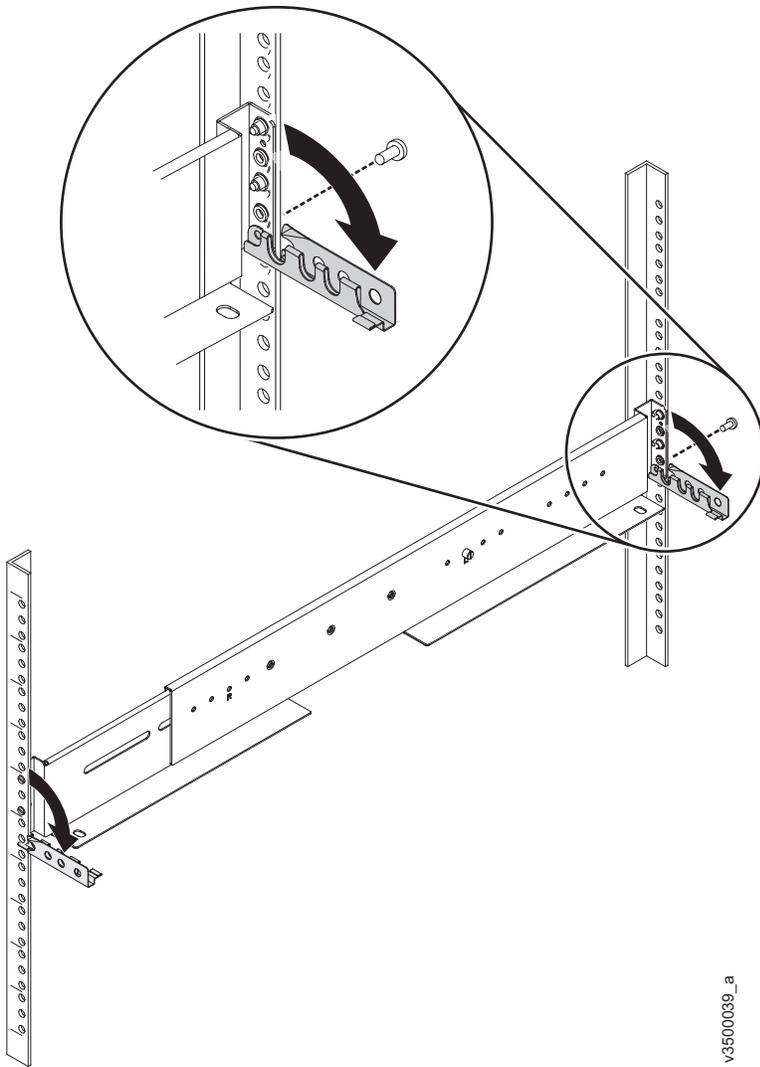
Abrindo o Suporte da Junta Traseiro de um Trilho de Montagem
